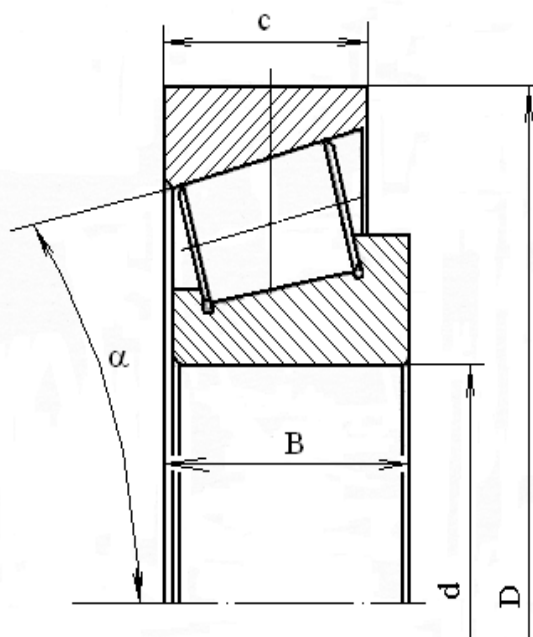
Подшипник роликовый радиально- упорный с коническими роликами
